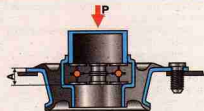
Проверка упругой деформации (осадки) верхней опоры: А — контрольный размер
